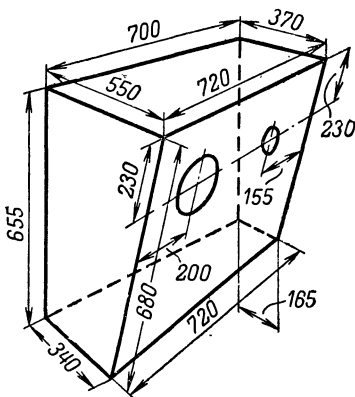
Конструктивный чертеж ящика агрегата.
